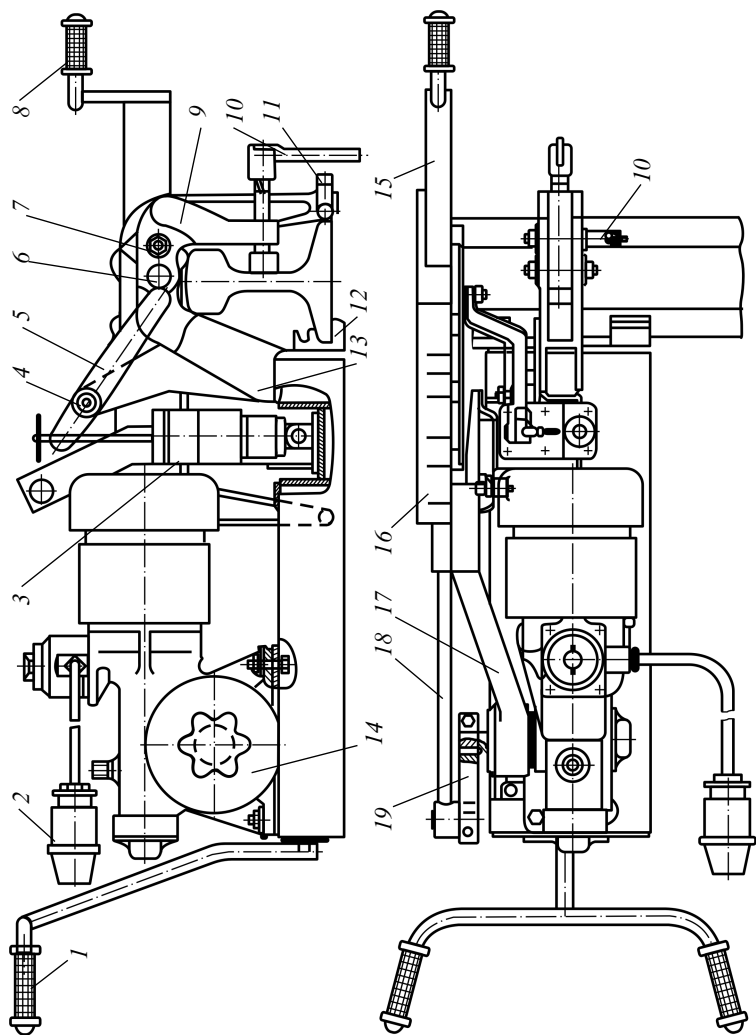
Рельсорезный станок РМ5ГМ:
